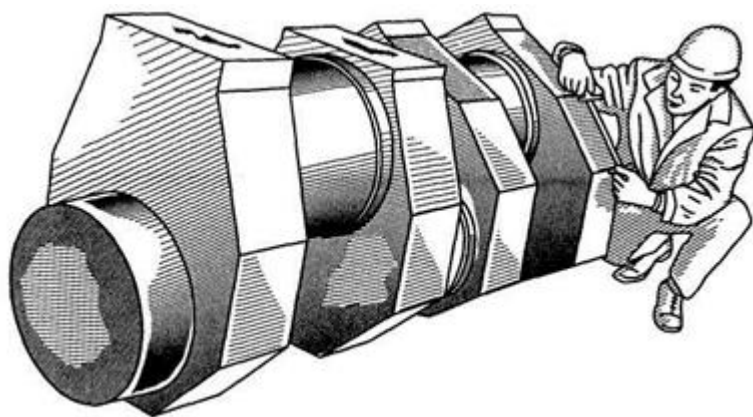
Коленчатый вал судового дизеля, изготовленный способом ЭШЛ
